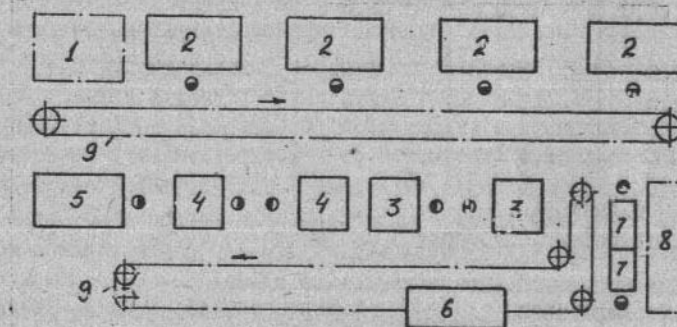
Участок с подвесными грузонесущими конвейерами: 1 - место для заготовок; 2-5 станки; 6 - моечная машина; 7 - позиции контроля; 8 - место для готовых деталей; 9 - подвесные грузонесущие конвейеры
